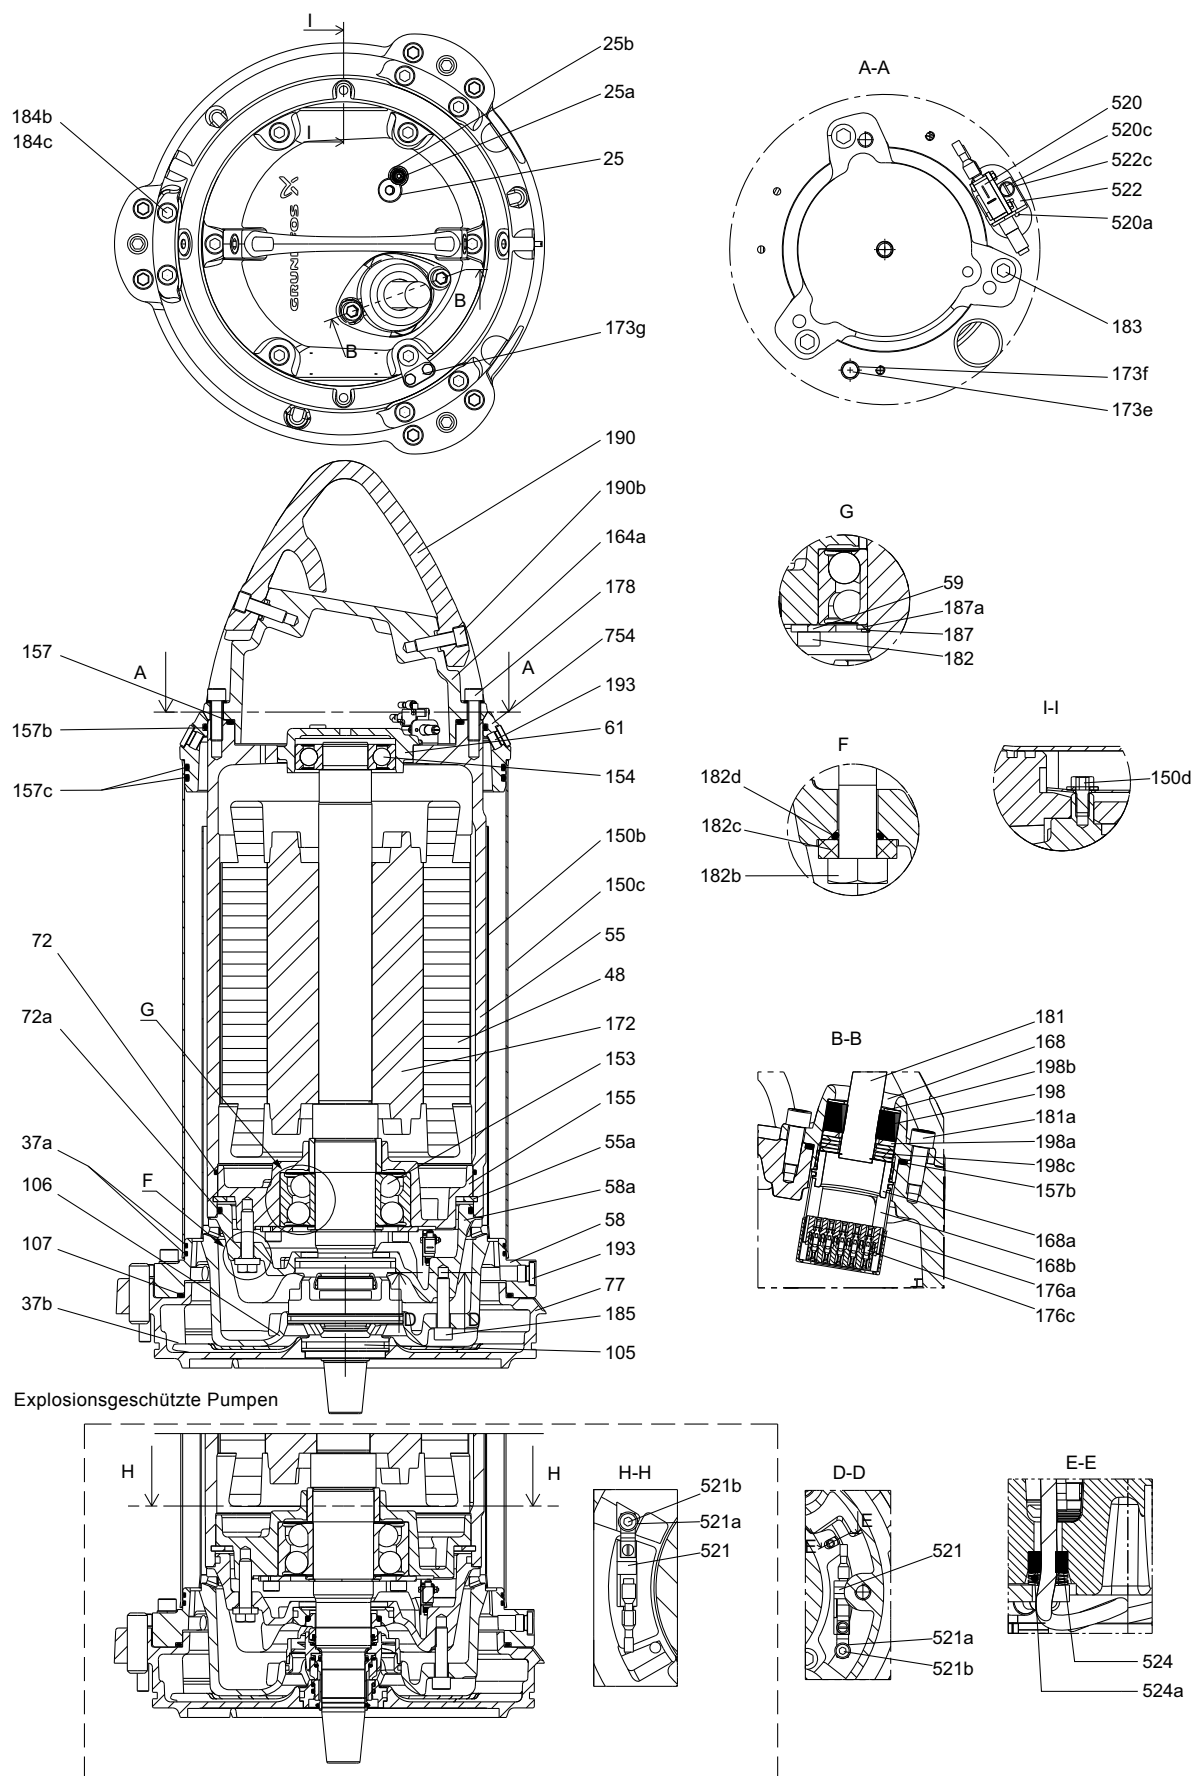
SE-Pumpen mit Kühlmantel mit 6-poligem Motor
